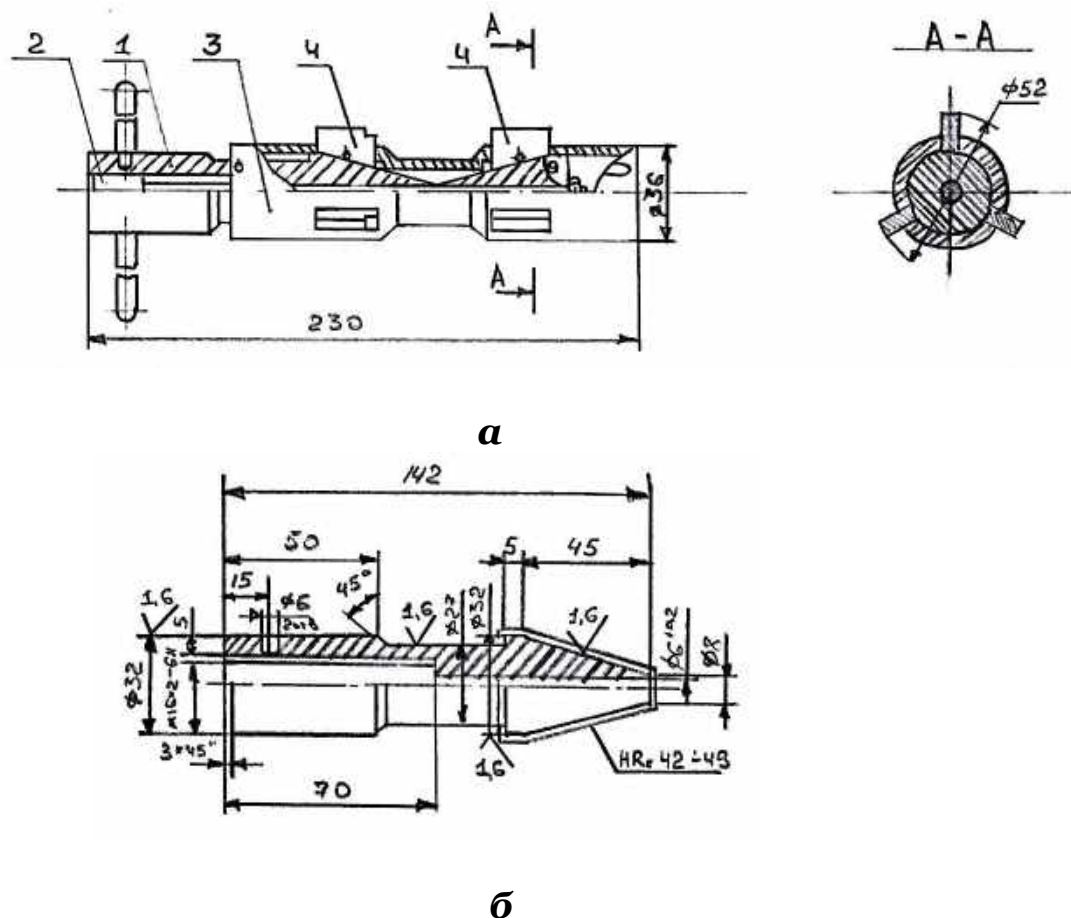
Центратор для труб діаметром $D = 38 - 70$ мм: а – загальна конструкція; б – робочий конус: 1 – конус; 2 – гайка; 3 – корпус; 4 – кулачок
